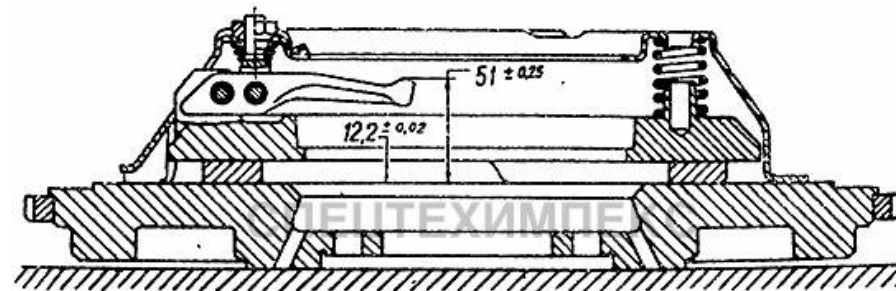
Регулировка рычагов выключения сцепления автомобиля ГАЗ-53.
